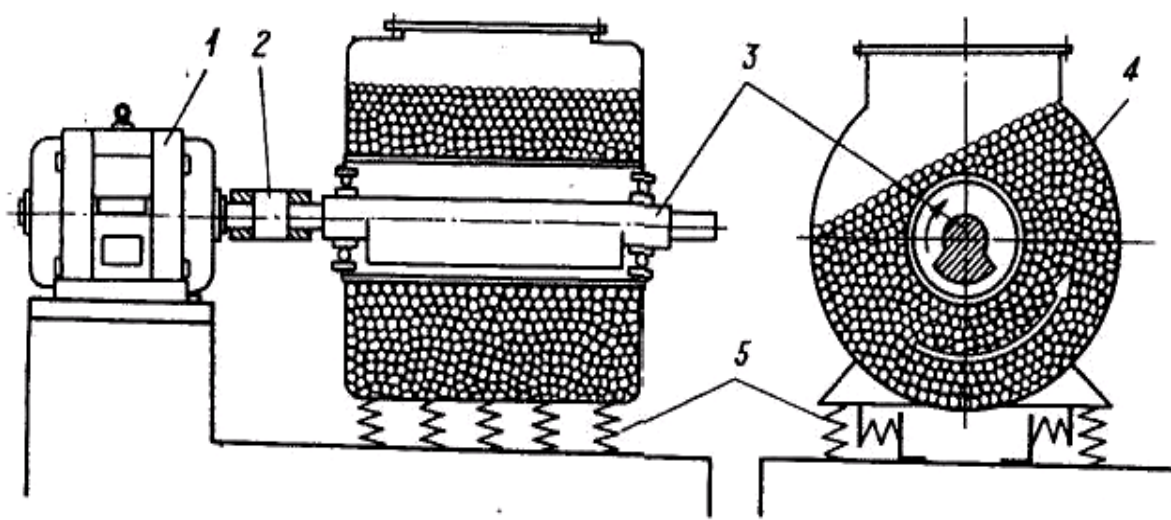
Схема вибромельницы: 1 – электродвигатель; 2 – эластичная муфта; 3 – вал с дебалансом; 4 – корпус; 5 – пружины
